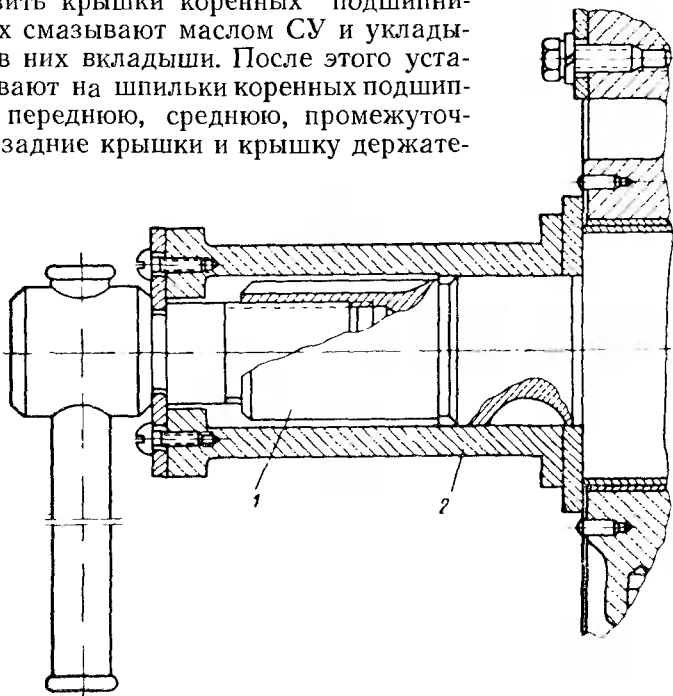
Приспособление для выравнивания торцов крышки первого коренного подшипника двигателя ЗМЗ-53:
